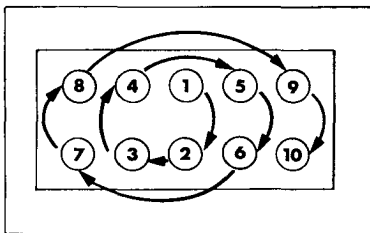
Последовательность затяжки болтов головки блока цилиндров
